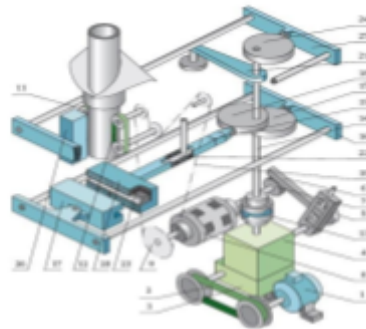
Пакувальна машина - автомат Roveta MVP із механічною САК: 1-електродвигун, 2-варіатор, 3-редуктор, 4-редуктор з двома валами, 5-кривошип, 6-зубчаста рейка, 7 – шестерня, 8- муфти, 9-зірочка, 10 –ланцюг транспортера, 11-12-транспортери протяжки, 13-муфта, 14-вал головний, 15- кулачок приводу передньої поперечної губки, 16-привід губки, 17-передня поперечна губка, 18,19,20 – кулачок, привід і сама задня поперечна губка, 21-штовхач приводу ножа, 22-привід ножа, 23-ніж, 24- кулачок приводу поздовжньої губки, 25-її привід, 26-поздовжня губка
